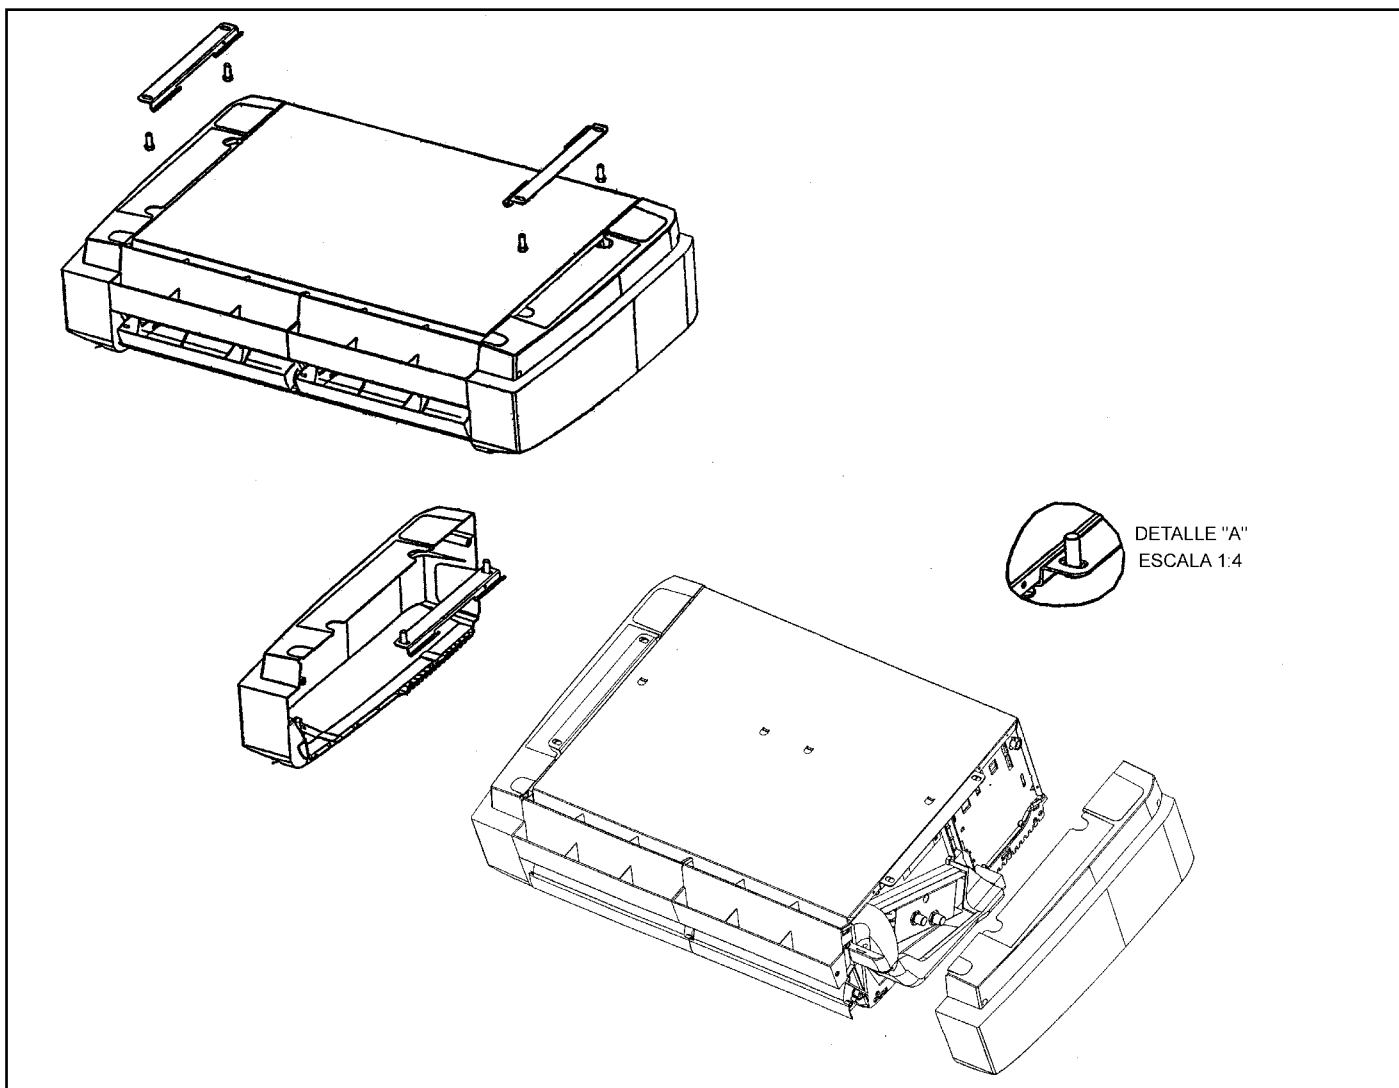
MONTAGEM DO SUPORTE DE FIXAÇÃO
